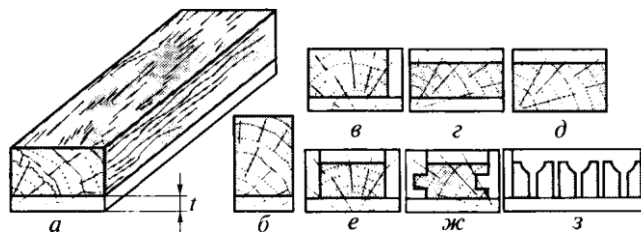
Види обробки на поздовжньо-фрезерних верстатах: а, б, в – фугувальних; г, д – рейсмусових; е, ж, з – чотирибічних
